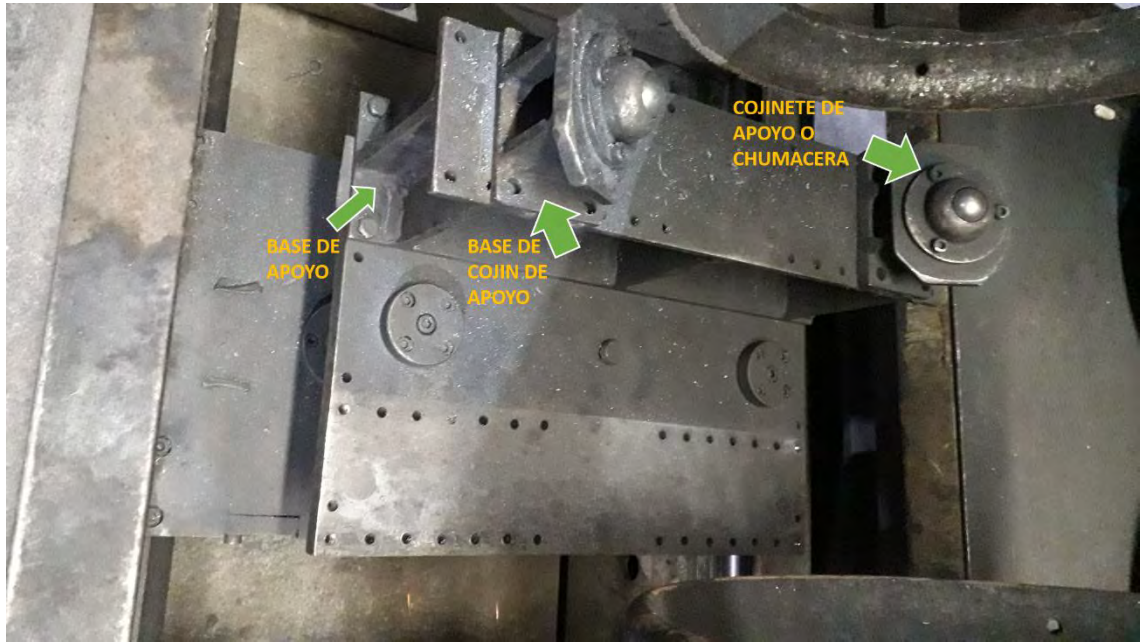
Componentes de la base de apoyo de la soldadora circular
